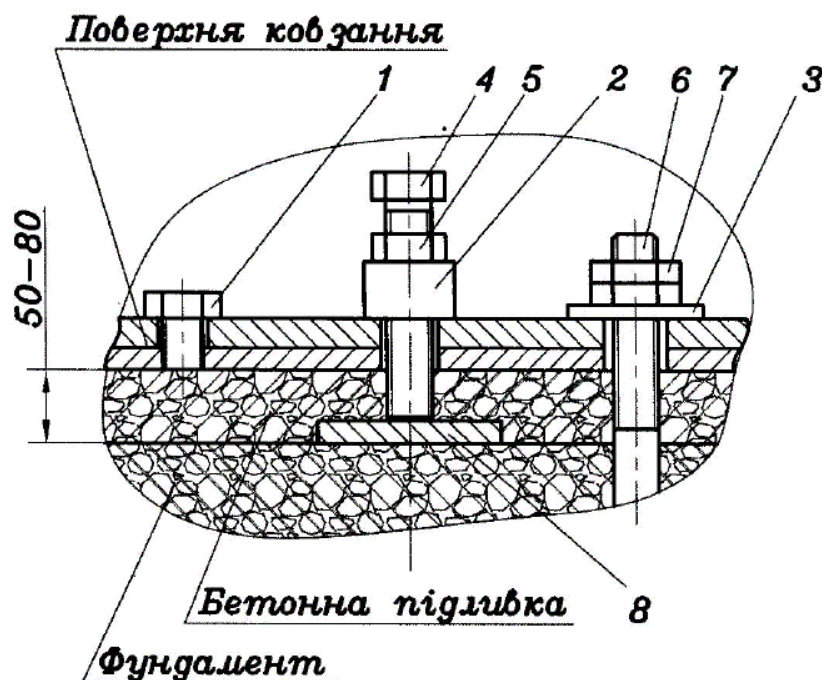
Кріплення опори: 1 – болт М16; 2 – втулка нарізна; 3 – шайба; 4 – гвинт регулювальний; 5 – гайка; 6 – болт фундаментний М24; 7 – гайка М24; 8 – пластина опорна
